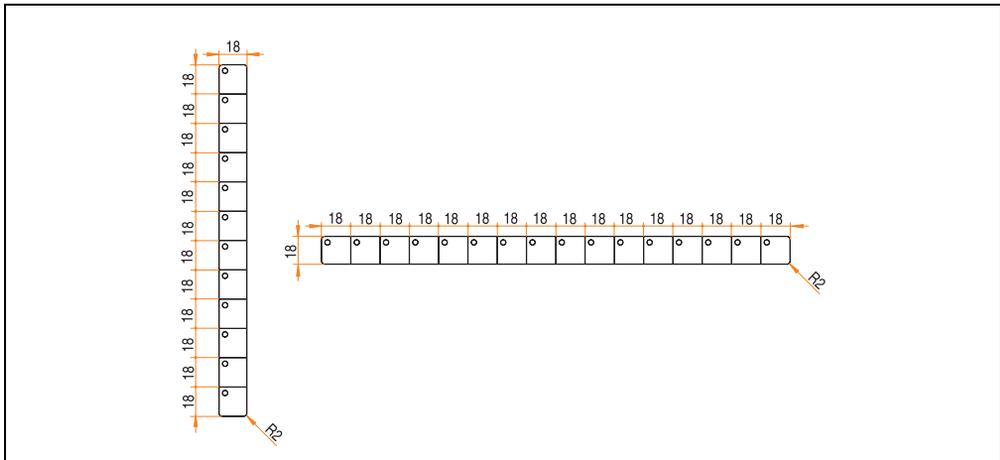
Tastenabmessungen - 5AP880.1505-00
